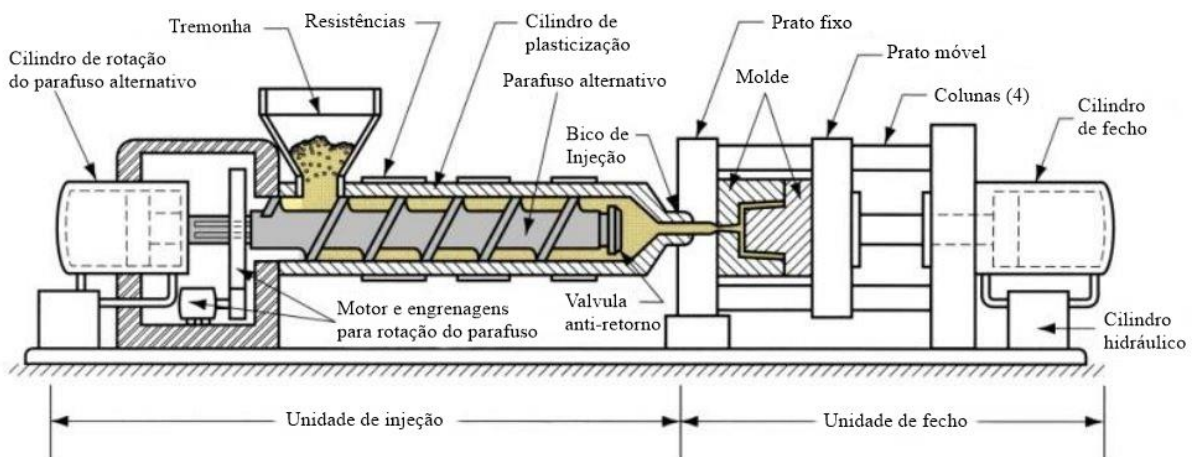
Máquina de injeção horizontal de parafuso alternativo. Adaptado de [6].
